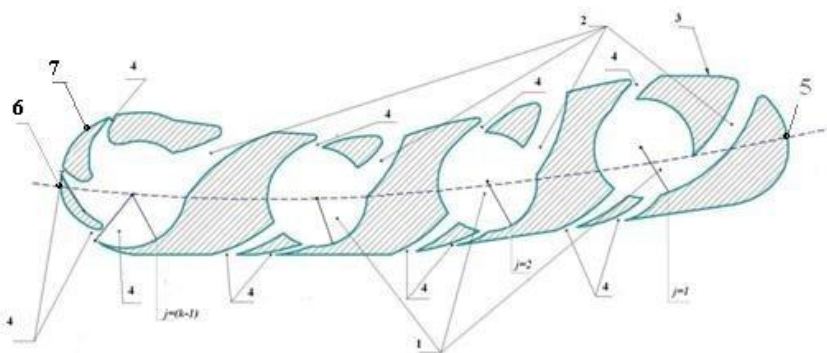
Лопатка рабочего колеса вентилятора местного проветривания с вихревыми камерами
